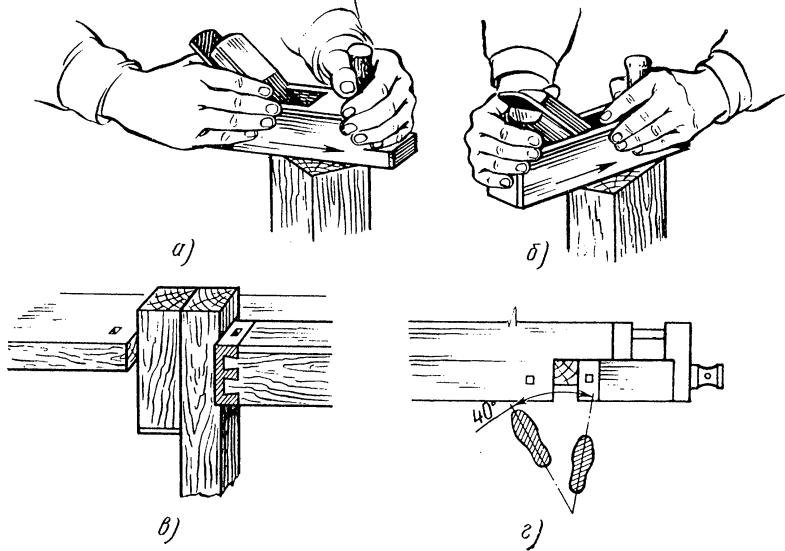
Торцевание заготовок с двух сторон до середины (а, б), с вспомогательным бруском (в) и положение ступней ног рабочего при торцевании (г)
